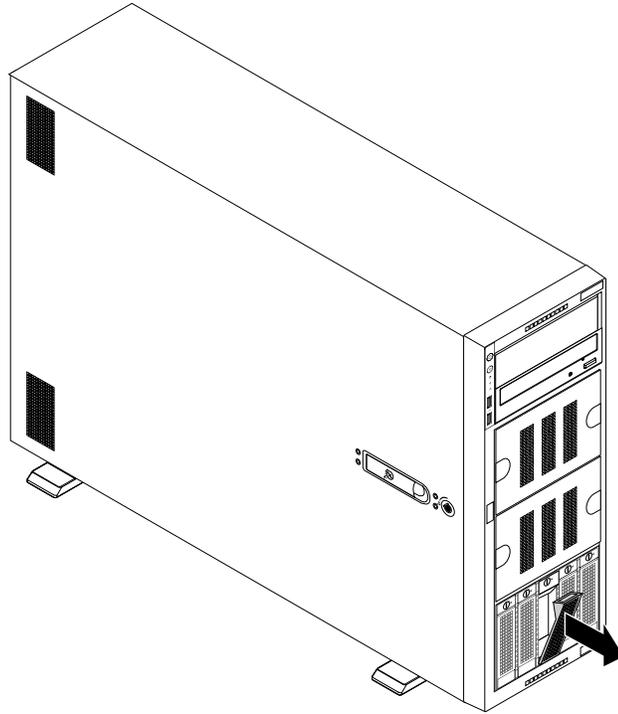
Retrait de l'unité remplaçable facilement ou du plateau factice
